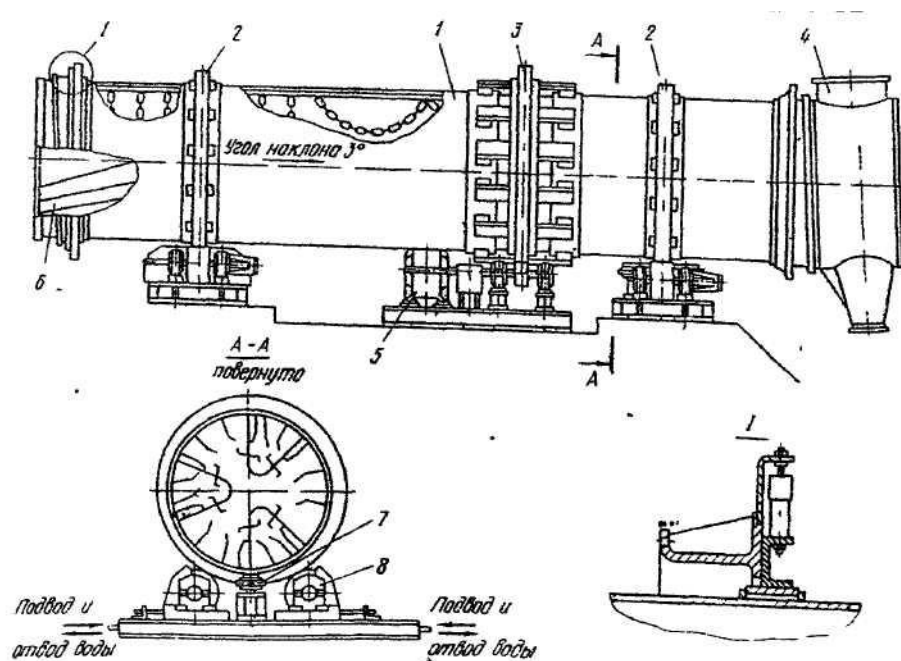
Барабанная сушилка: 1 – корпус; 2 – опорный бандаж; 3 – венцовая шестерня; 4 – разгрузочная камера; 5 – привод; 6 – секция насадки с гребками; 7 – опорный ролик; 8 – упорный ролик
